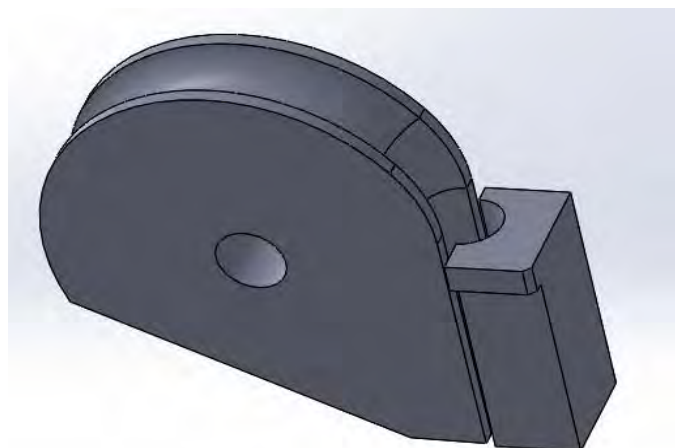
Modelado de opresor para dado 29 mm. hecho en SolidWorks. Se muestra como se colocará el opresor y cómo funcionará el desplazamiento realmente.
